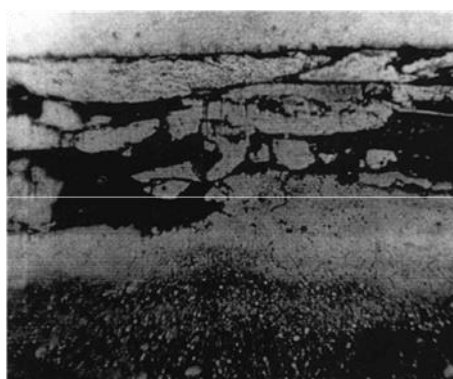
Изношенный молоток кормодробилки из стали 65Г
